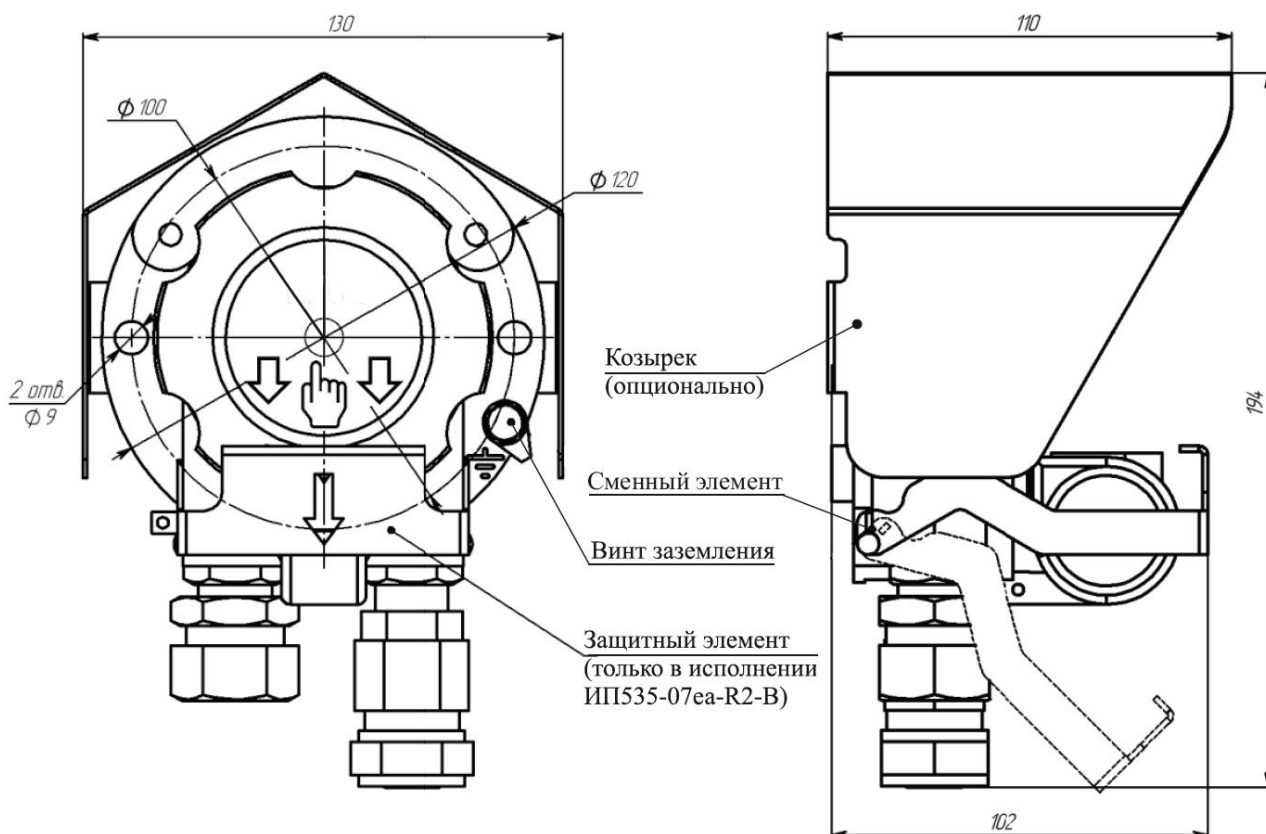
Установка ИП535-07ea-R2
